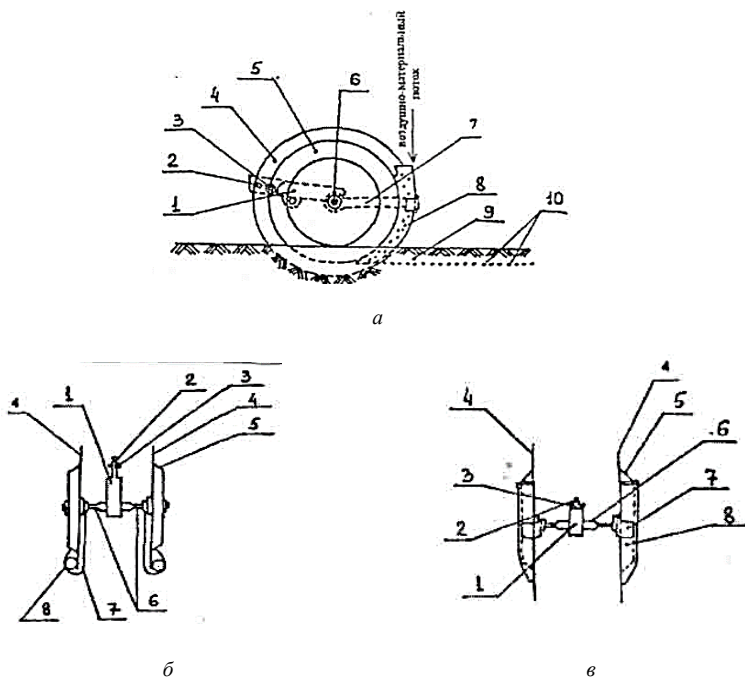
Двухдисковый сошник с внешними конусными ребрами и нулевым углом атаки дисков: *а* – вид сбоку; *б* – вид сверху; *в* – вид сзади; 1 – корпус; 2 – отверстие; 3 – болт; 4 – диски; 5 – реборды-бороздкообразователи-уплотнители; 6 – ось; 7 – пластина; 8 – семянаправитель; 9 – бороздка; 10 – семена
